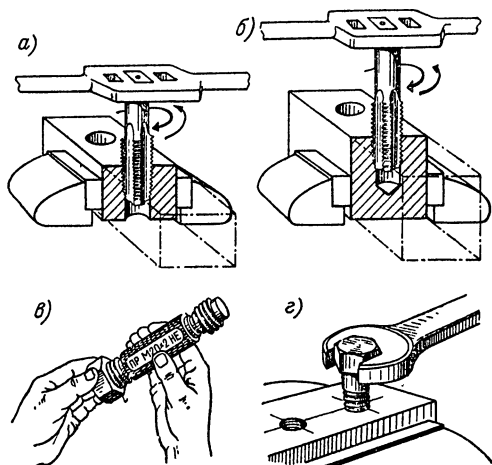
Приемы нарезания и контроля внутренней резьбы
